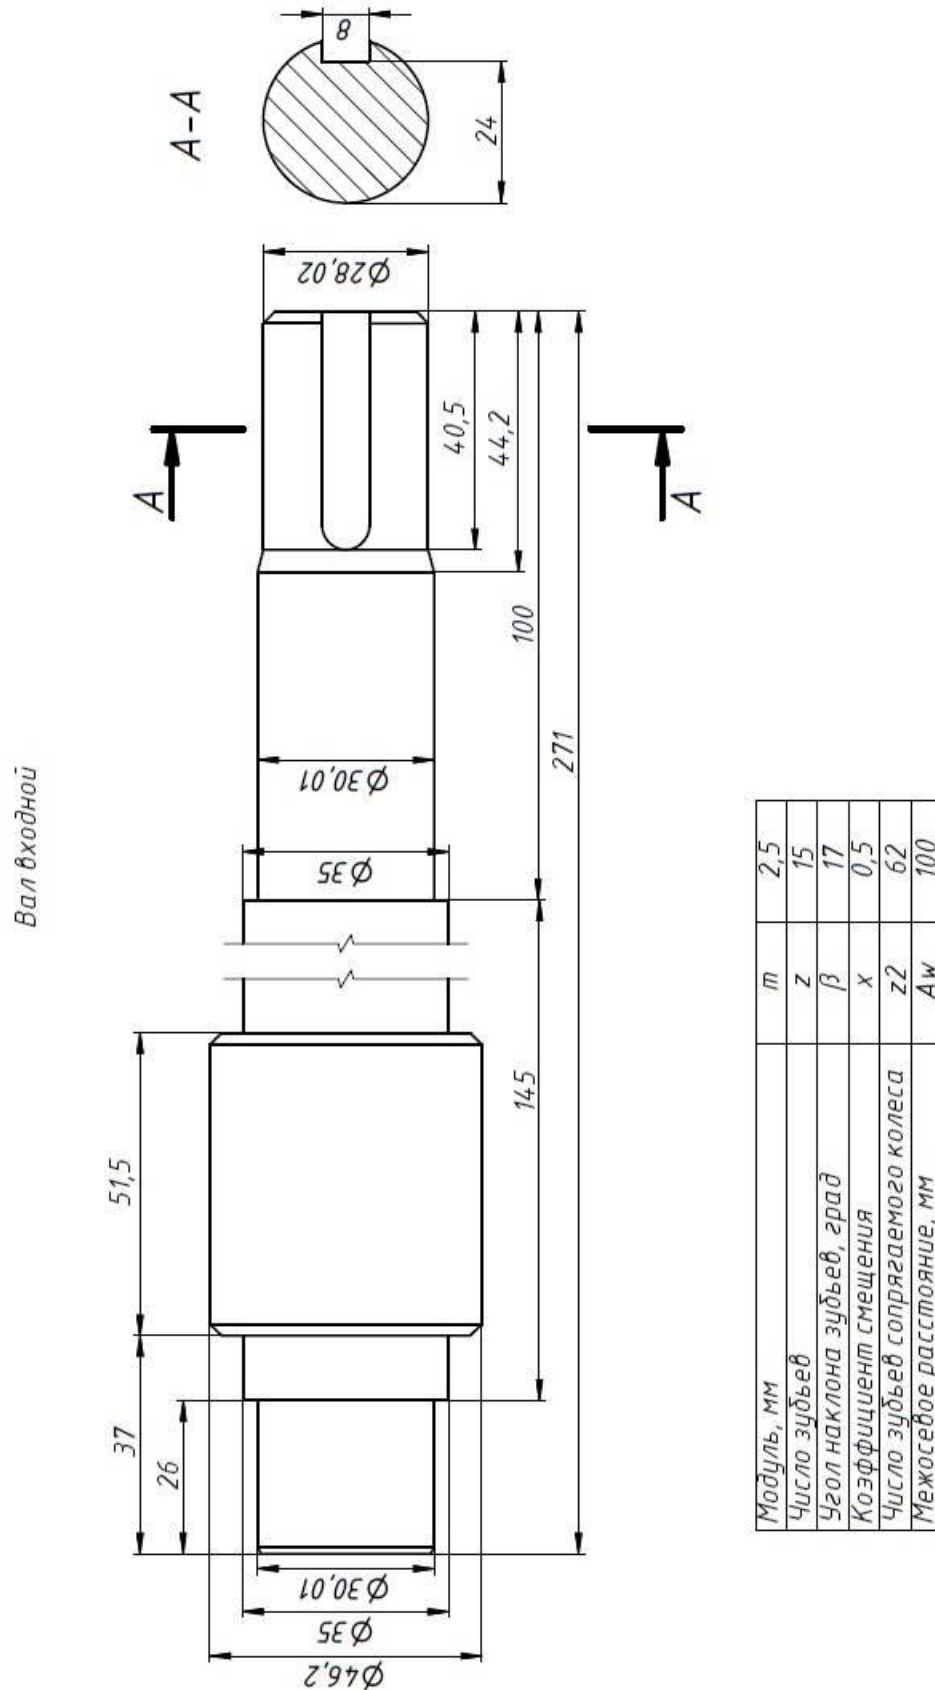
Чертеж вала-шестерни входной редуктора с эвольвентным зубчатым зацеплением
